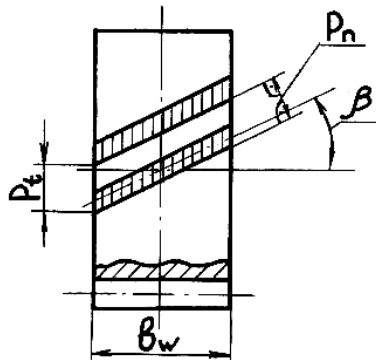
Развертка поверхности делительного цилиндра на плоскость
